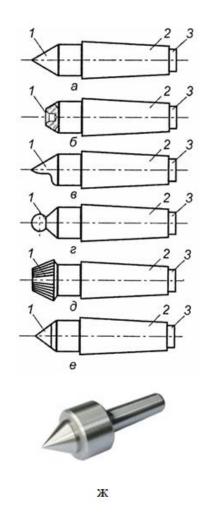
Центры для токарных станков: а — опорный, б — обратный, в — срезанный, г — шариковый, д — рифленый, е — опорный твердосплавный, ж — вращающийся
